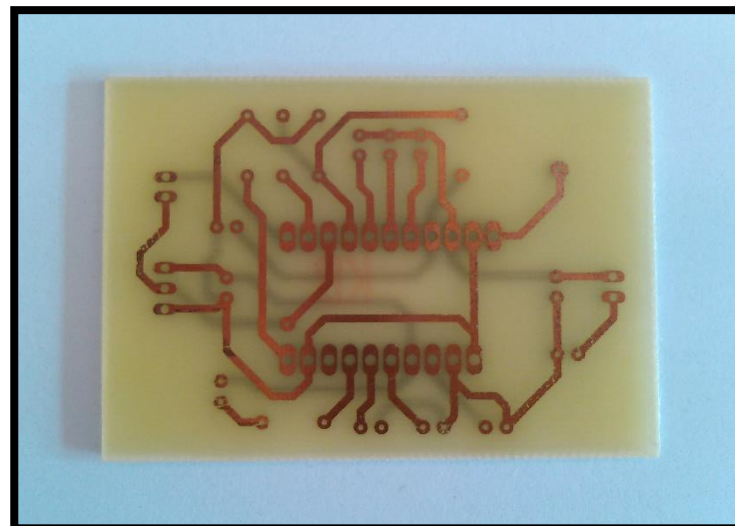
PCB del circuito del chip bq51050B sin montar (BOTTOM)
